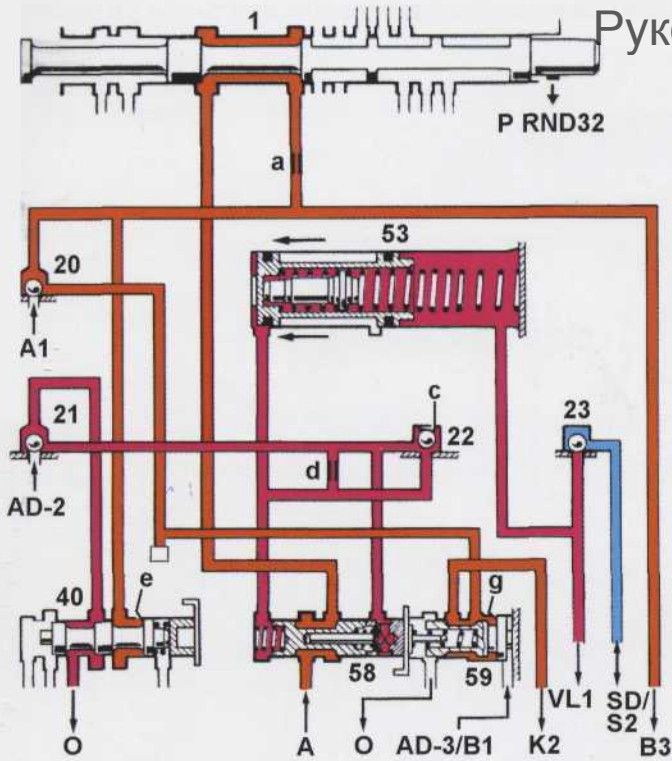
Работа системы аккумулятора включения при установке рычага выбора диапазона в положение "R". 1 - Клапан выбора диапазона; 20 - Распределительный шариковый клапан; 21 - Распределительный шариковый клапан; 22 - Обратный шариковый клапан; 23 - Обратный шариковый клапан; 40 - Клапан принудительного понижения передачи; 53 - Аккумулятор переключения; 58 - Клапан включения; 59 - Клапан включения муфты K2; A - Рабочее давление; A1 - Рабочее давление на 1-ой передаче; AD-2 - Рабочее давление на диапазонах "D", "3" и "2"; AD-3/B1 - Рабочее давление на диапазонах "D" и "3" или включенном ленточном тормозе B1; K2 - Канал к бустеру муфты K2; O - Слив в поддон; SD/S2 - Давление подпора или давления управления клапана-дросселя (в зависимости от исполнения клапанной коробки); VL1 - Канал к сливному сечению плунжера клапана-дросселя (46); a, d - Жиклеры; c - Пружина; e, f, g - Кольцевые канавки.
